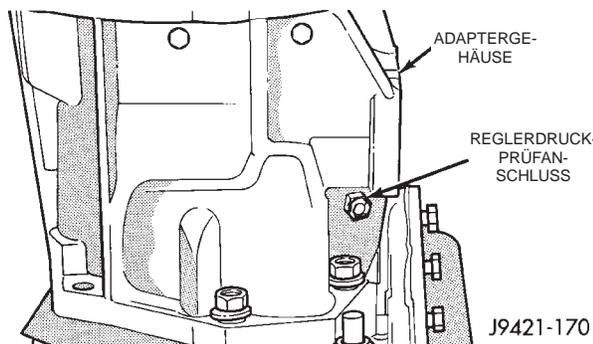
Druckprüfanschlüsse auf der Gehäuse-Rückseite—Allradantrieb
